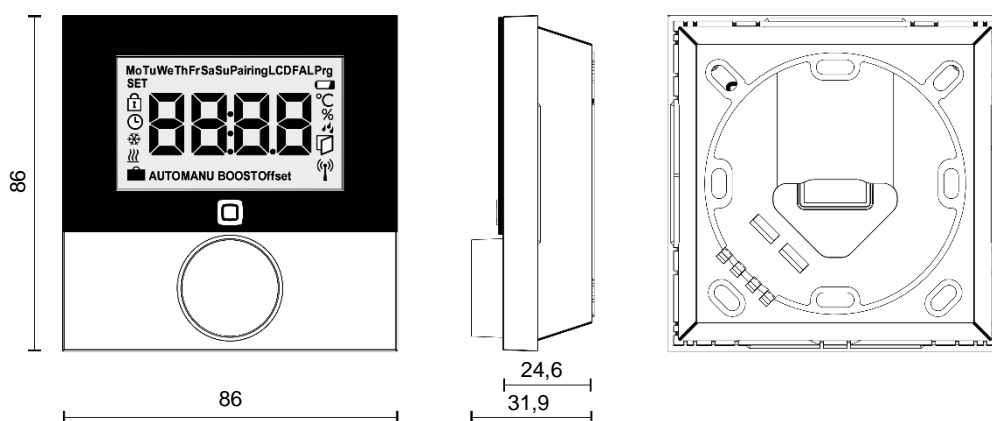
Dimensioner COMFORT IP: Digital rumtermostat (dimensioner er i mm)
